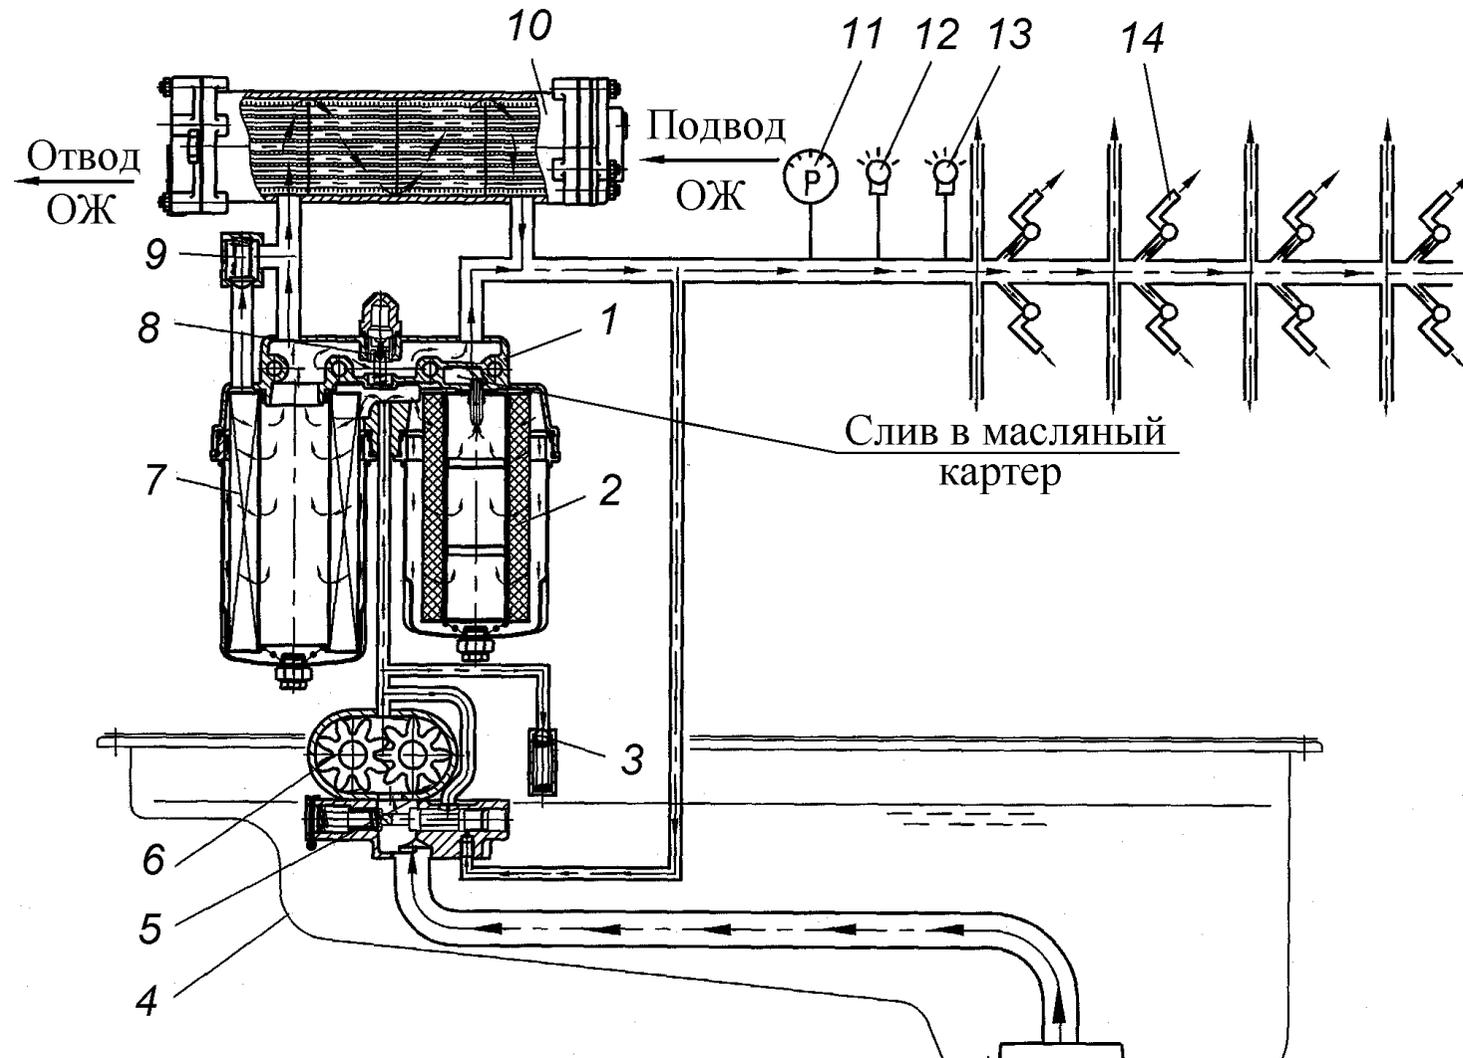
Схема смазочной системы двигателя 740.50-360:
